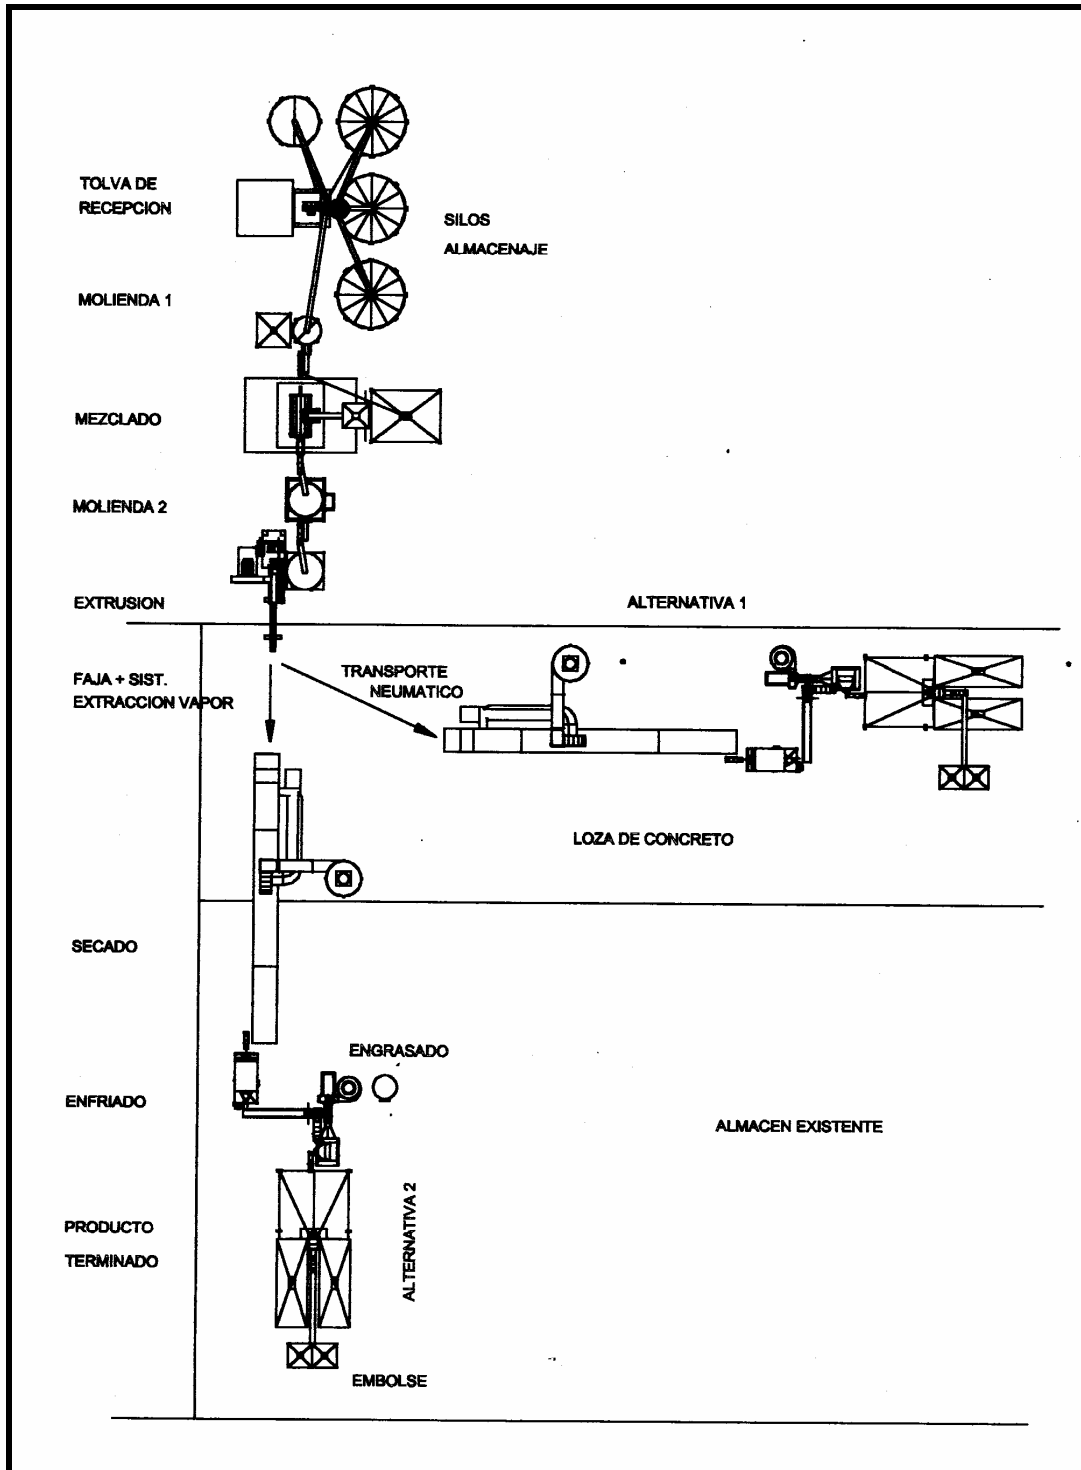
Distribución de planta alternativa 1, alternativa 2.
